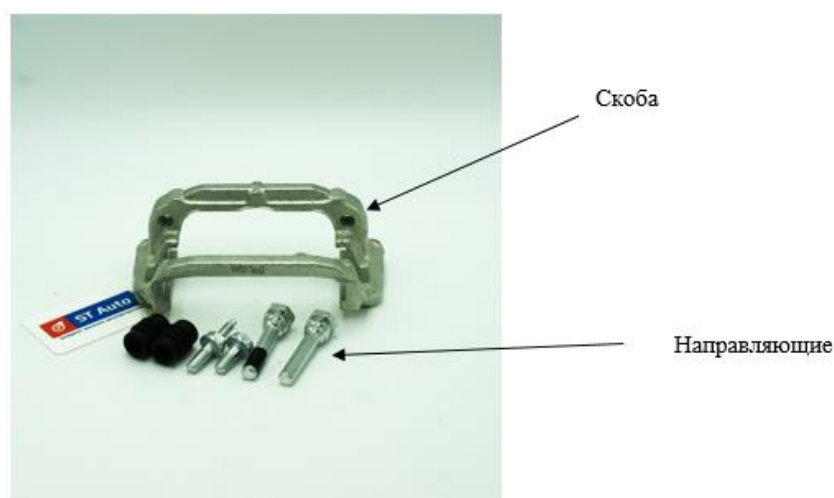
Скоба суппорта и направляющие пальцы тормозного механизма
